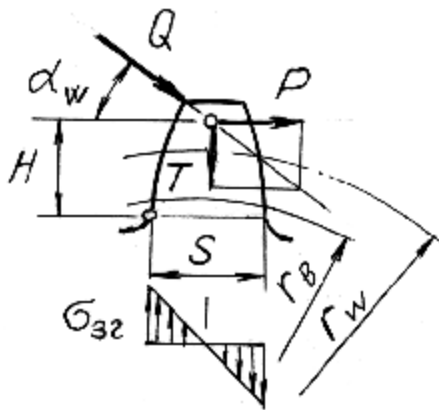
Схема для розрахунку напруження згину в зубцях циліндричного зубчастого колеса
